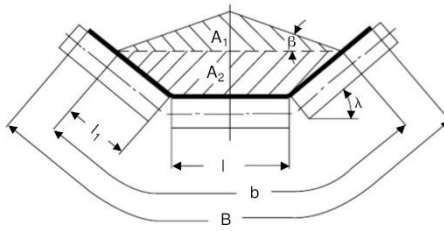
Área de la Sección Transversal. Fuente: Ingemecanica, 2021.
